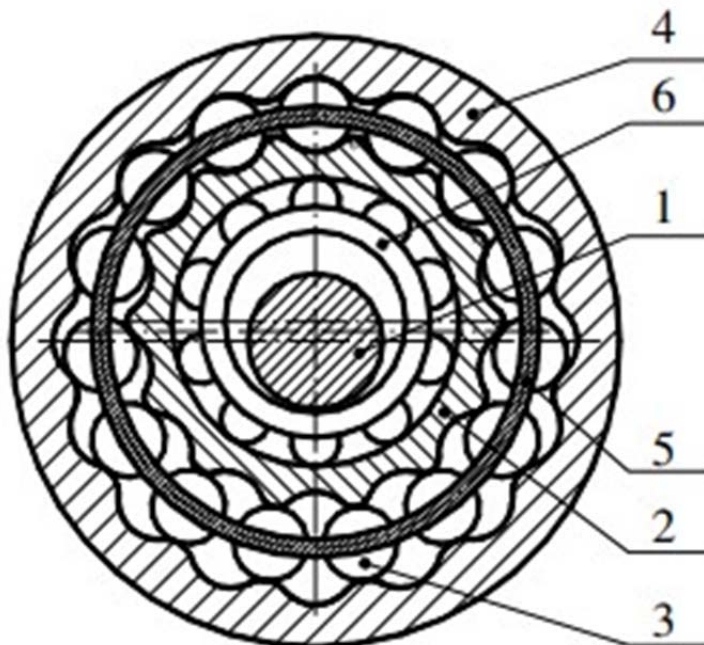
Схема передачи с промежуточными телами качения и свободной обоймой
